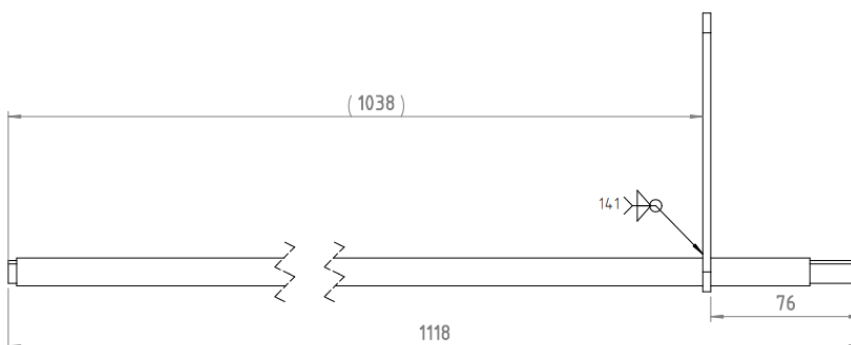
Definição de soldadura do conjunto veio motriz e braço
